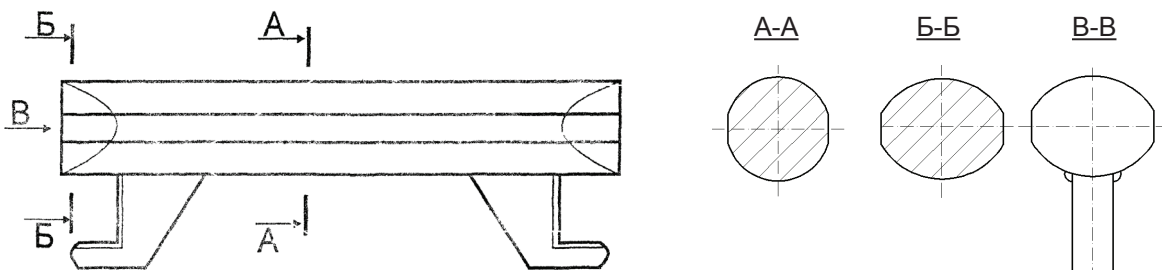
Колосник [11], изготовленный методами прокатки верхней части и сварки с нижней частью
